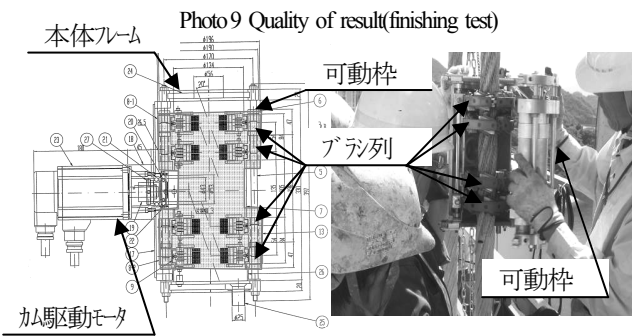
本装置断面図(4段) 写真-10 本装置内部状況写真
